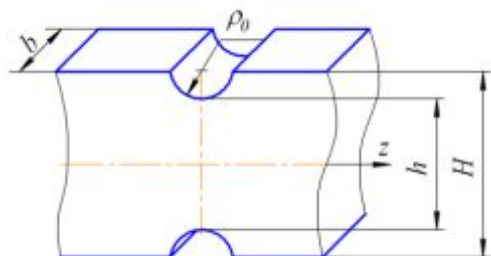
Рабочая часть образца прямоугольного поперечного сечения для испытаний на усталость
